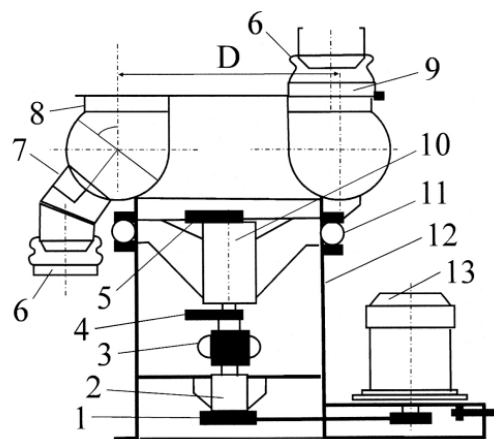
Вибрационный смеситель-измельчитель типа СМВ: 1 – клиноременная передача; 2 – промежуточная опора; 3 – упругая муфта; 4,5 – нижний и верхний дебаланс; 6 – герметизатор; 7 – клапан разгрузки; 8 – камера; 9 – патрубок загрузки; 10 – вибровозбудитель; 11 – упругие элементы; 12 – рама; 13 – электродвигатель
